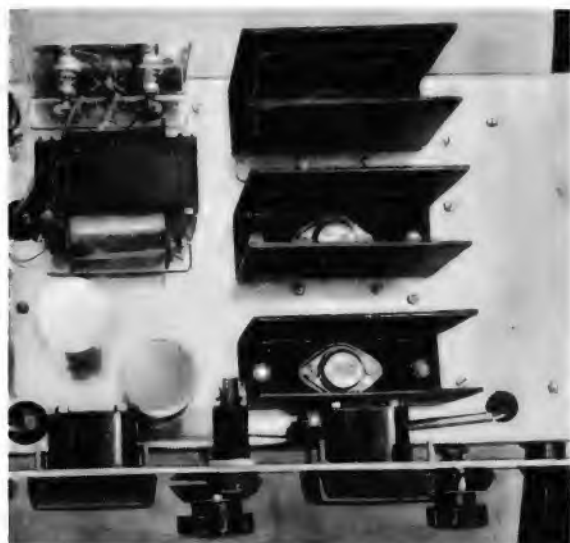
Die Teilansicht des Chassisaufbaus zeigt die Montage der Hauptstrom-Transistoren OC 29 mit ihren U-förmigen Kühlblechen
